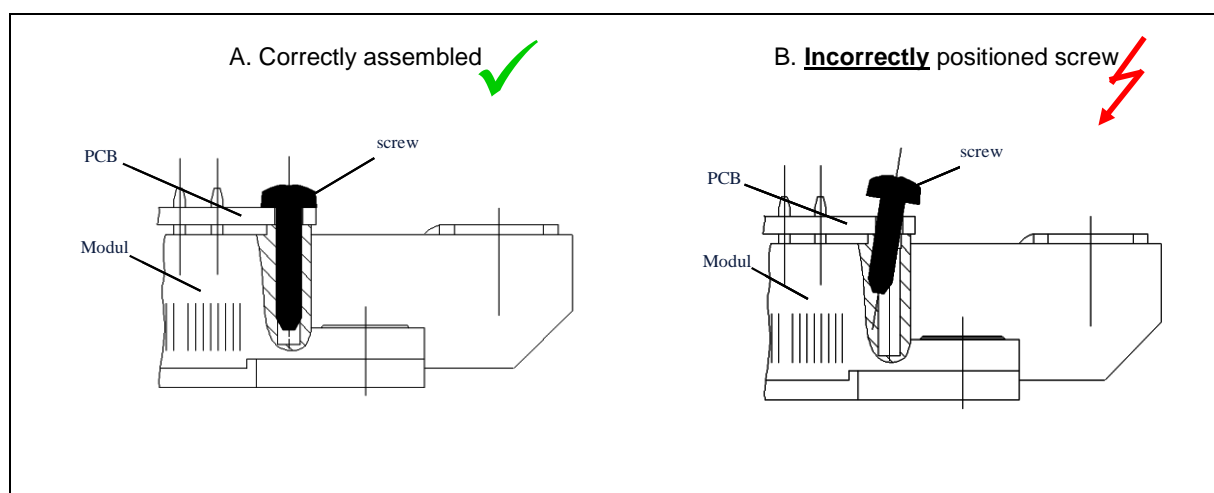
A. 正确地将螺丝拧入 PCB 电路板安装支脚
